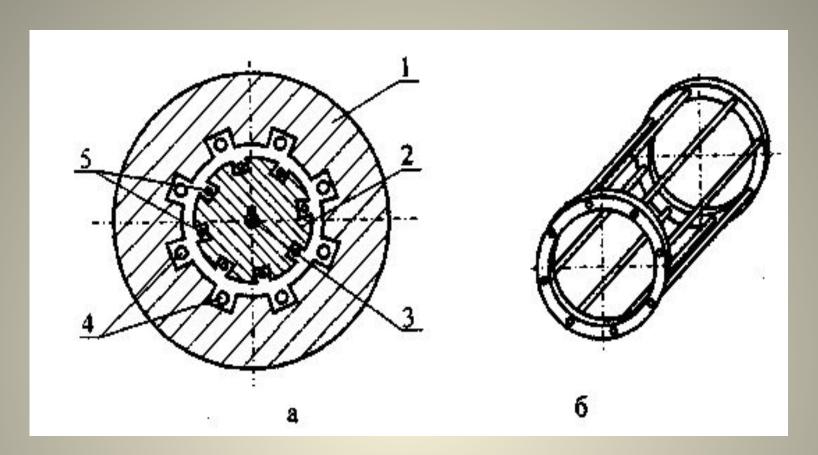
Схема устройства асинхронного двигателя: поперечный разрез (a); обмотка ротора(б): 1 – статор; 2 – ротор; 3 – вал; 4 – витки обмотки статора; 5 – витки обмотки ротора
